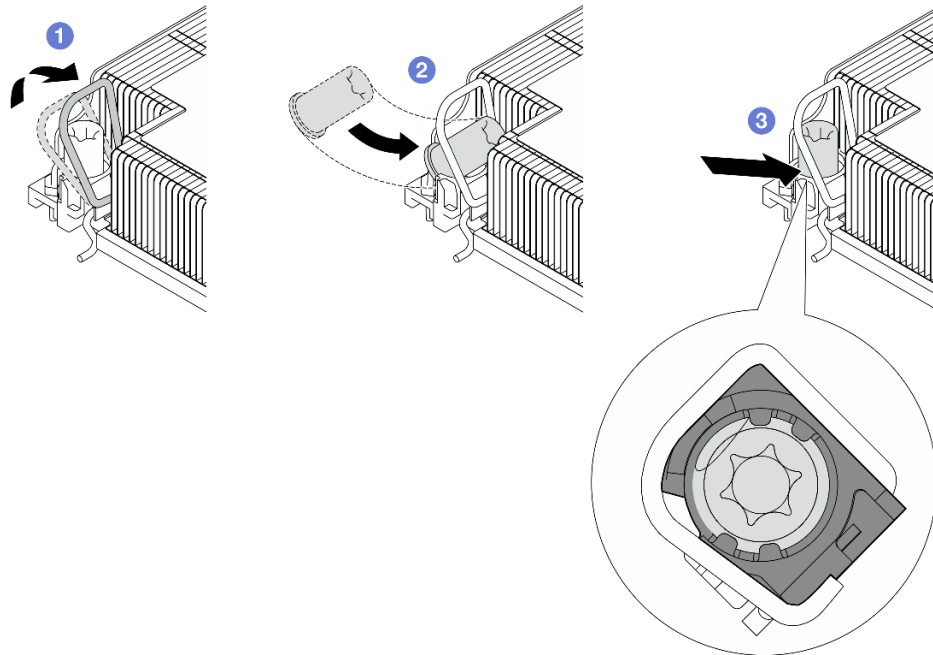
Instalación de una tuerca Torx T30 en el disipador de calor
